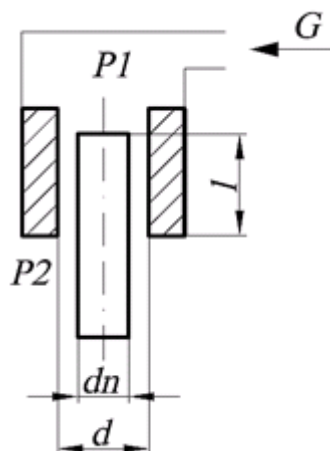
Схема пневмосопротивления плунжерного типа
